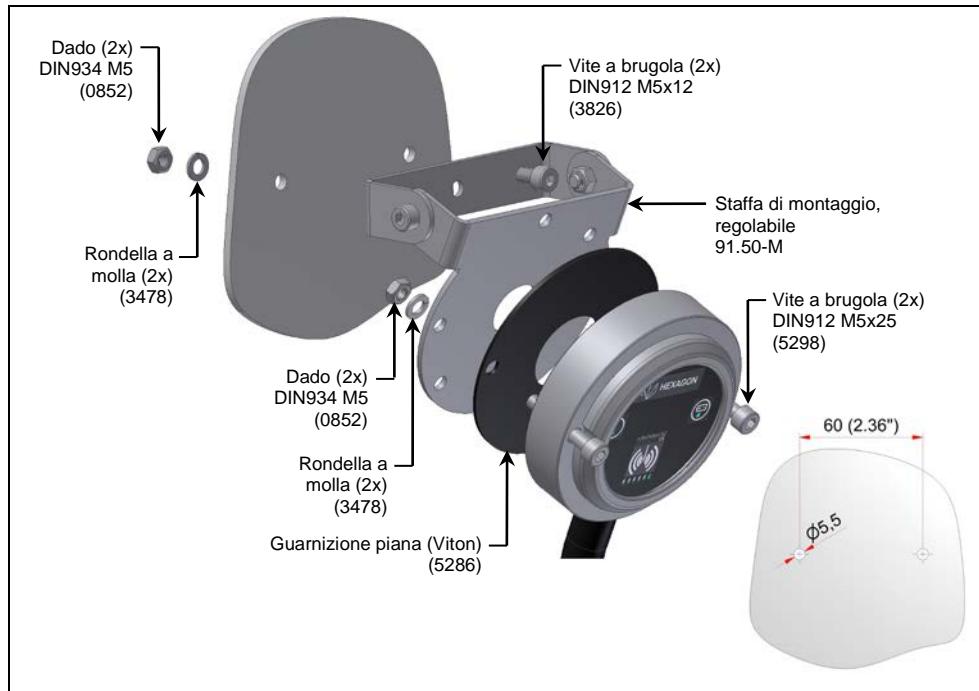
Montaggio RWR95.50-R con staffa di montaggio
